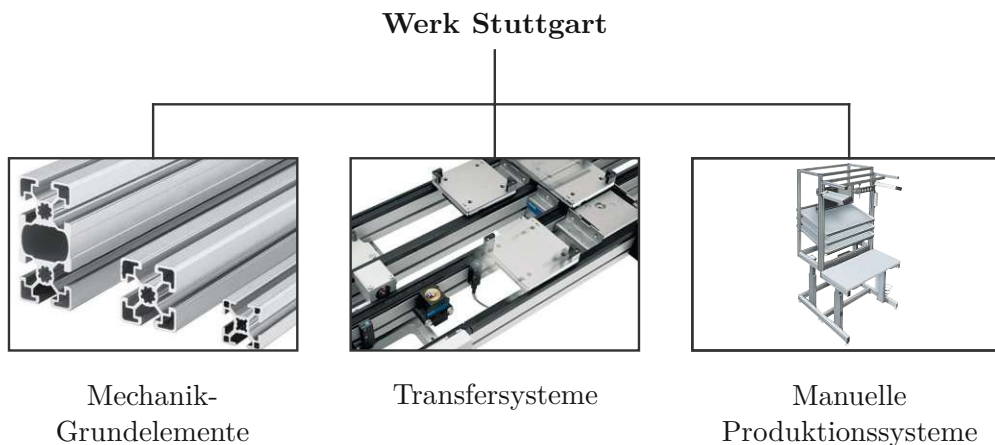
Erzeugnisgruppen des Werk Stuttgarts
